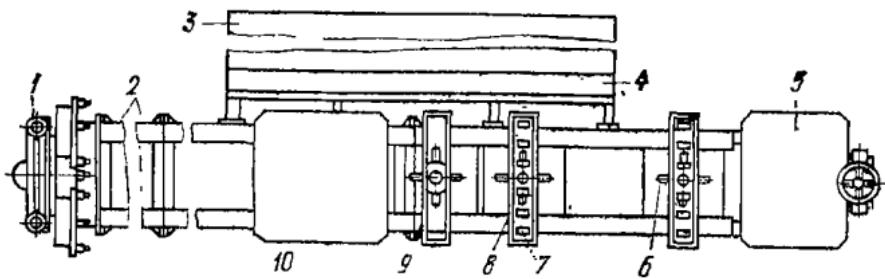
Стенд 13520 для сборки элементов трубопроводов:
